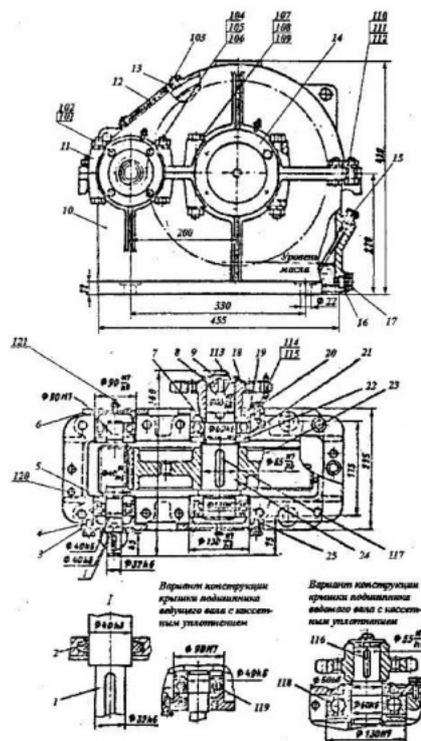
Цилиндрический одноступенчатый зубчатый редуктор
